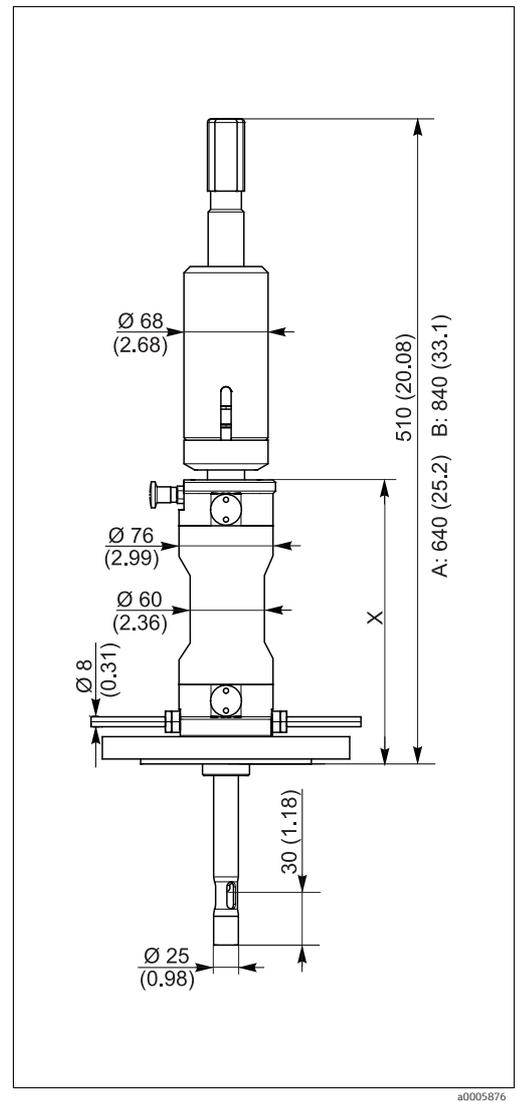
Version : standard pour capteurs à remplissage KCl.
